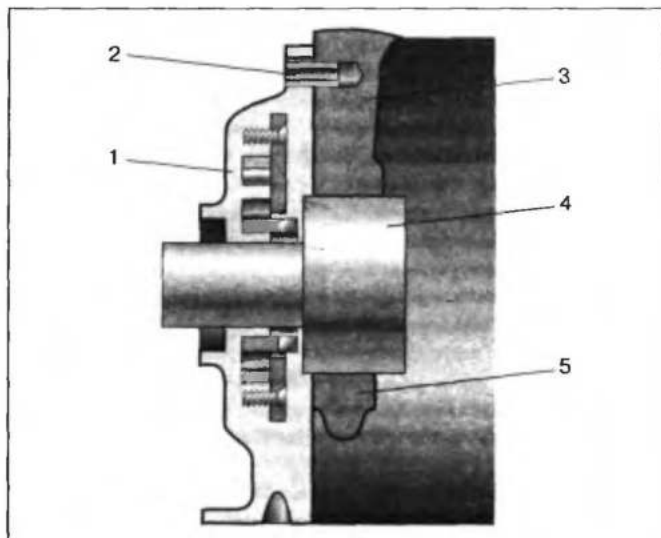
Схема центрирования корпуса масляного насоса на блоке цилиндров:
